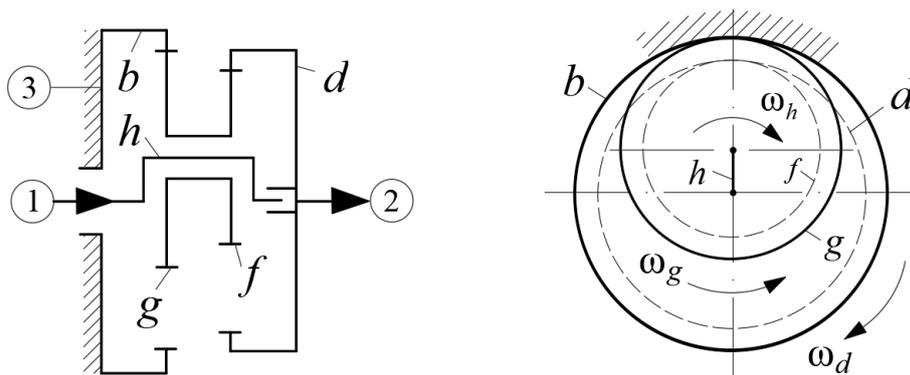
Трехзвенный планетарно-кривошипный механизм эвольвентного зацепления с двухзвенцовым сателлитом
